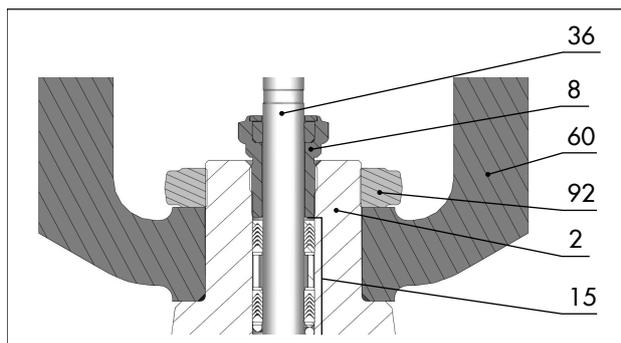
Packung mit Gewindebuchse zentral verschraubt (Beispieldarstellung)
